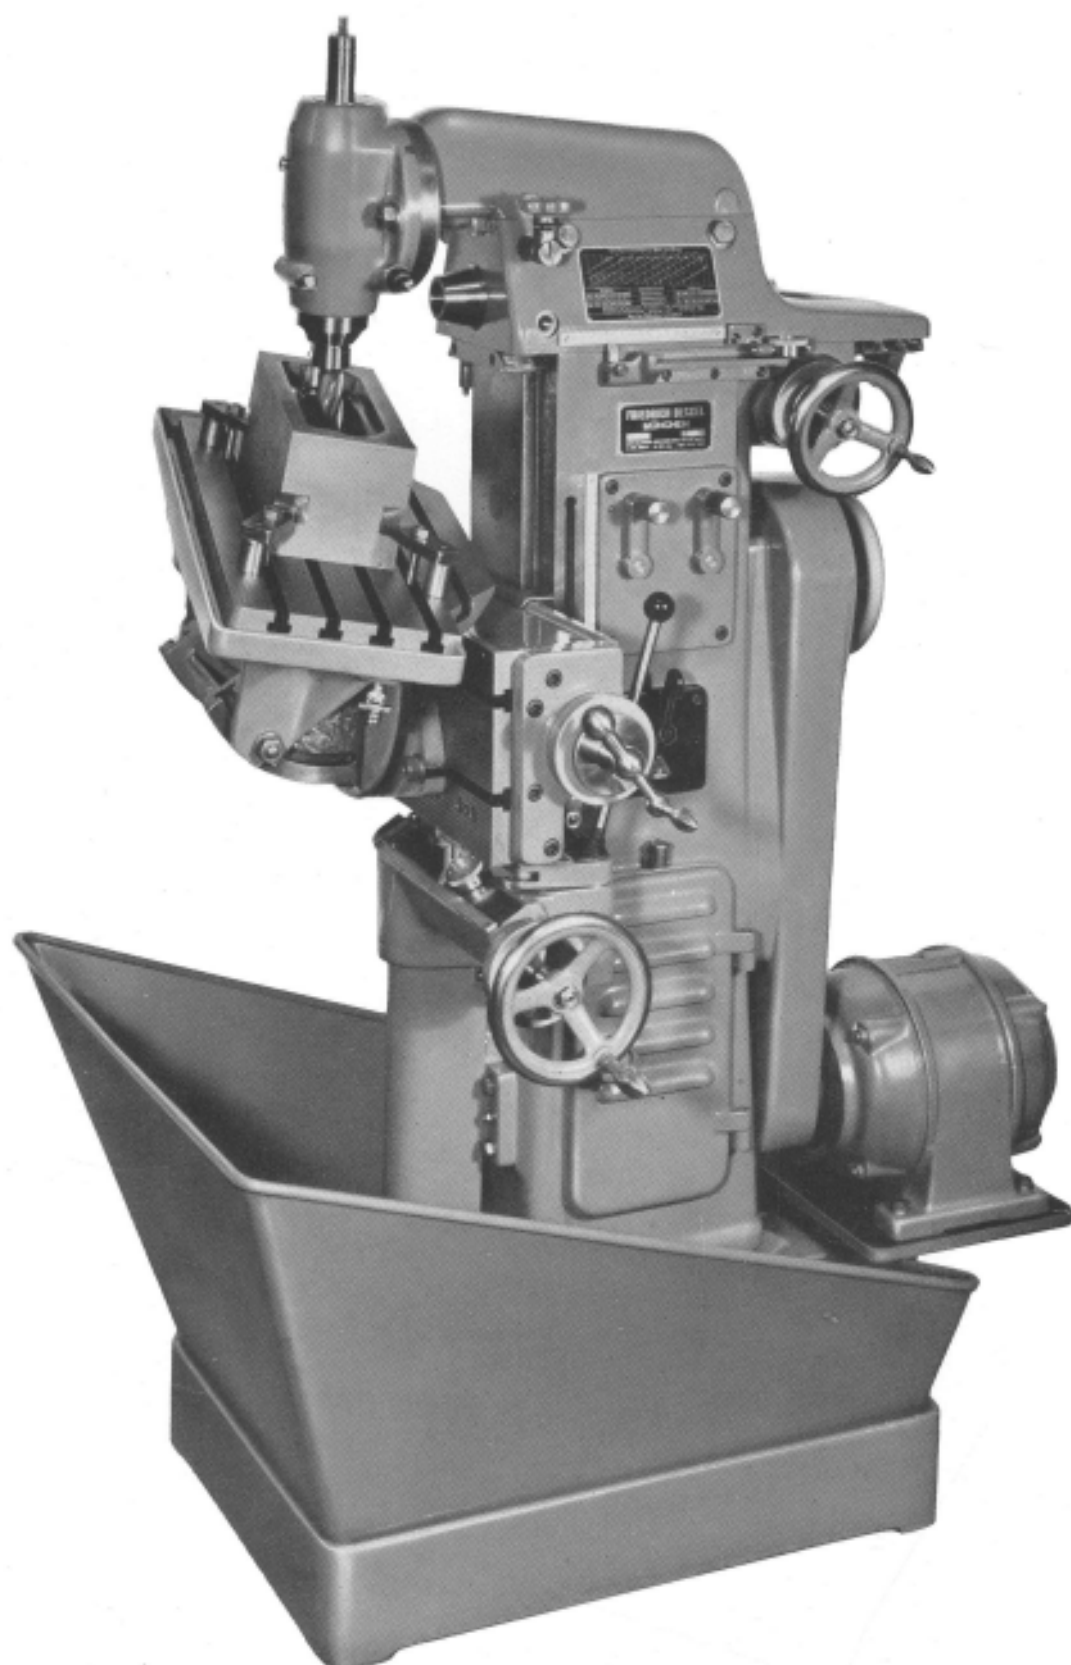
Universal-Werkzeug-Fräsmaschine FP 1
